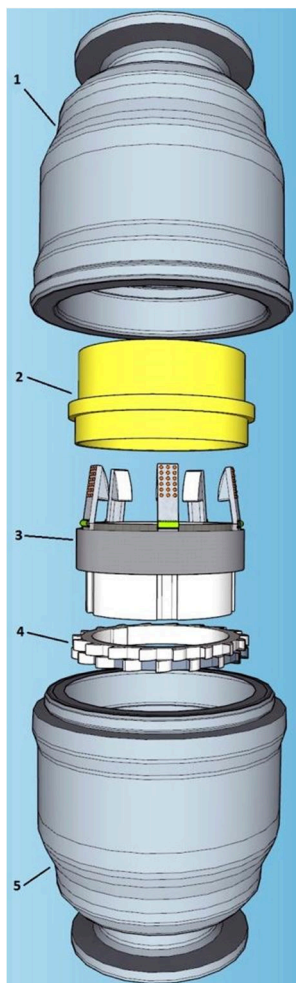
Пилотная конструкция инструмента для вращающегося превентора, состоящая: из верхнего корпуса 1; плунжера 2; шлифовальной установки 3; гидравлической турбины 4 и нижнего корпуса 5
